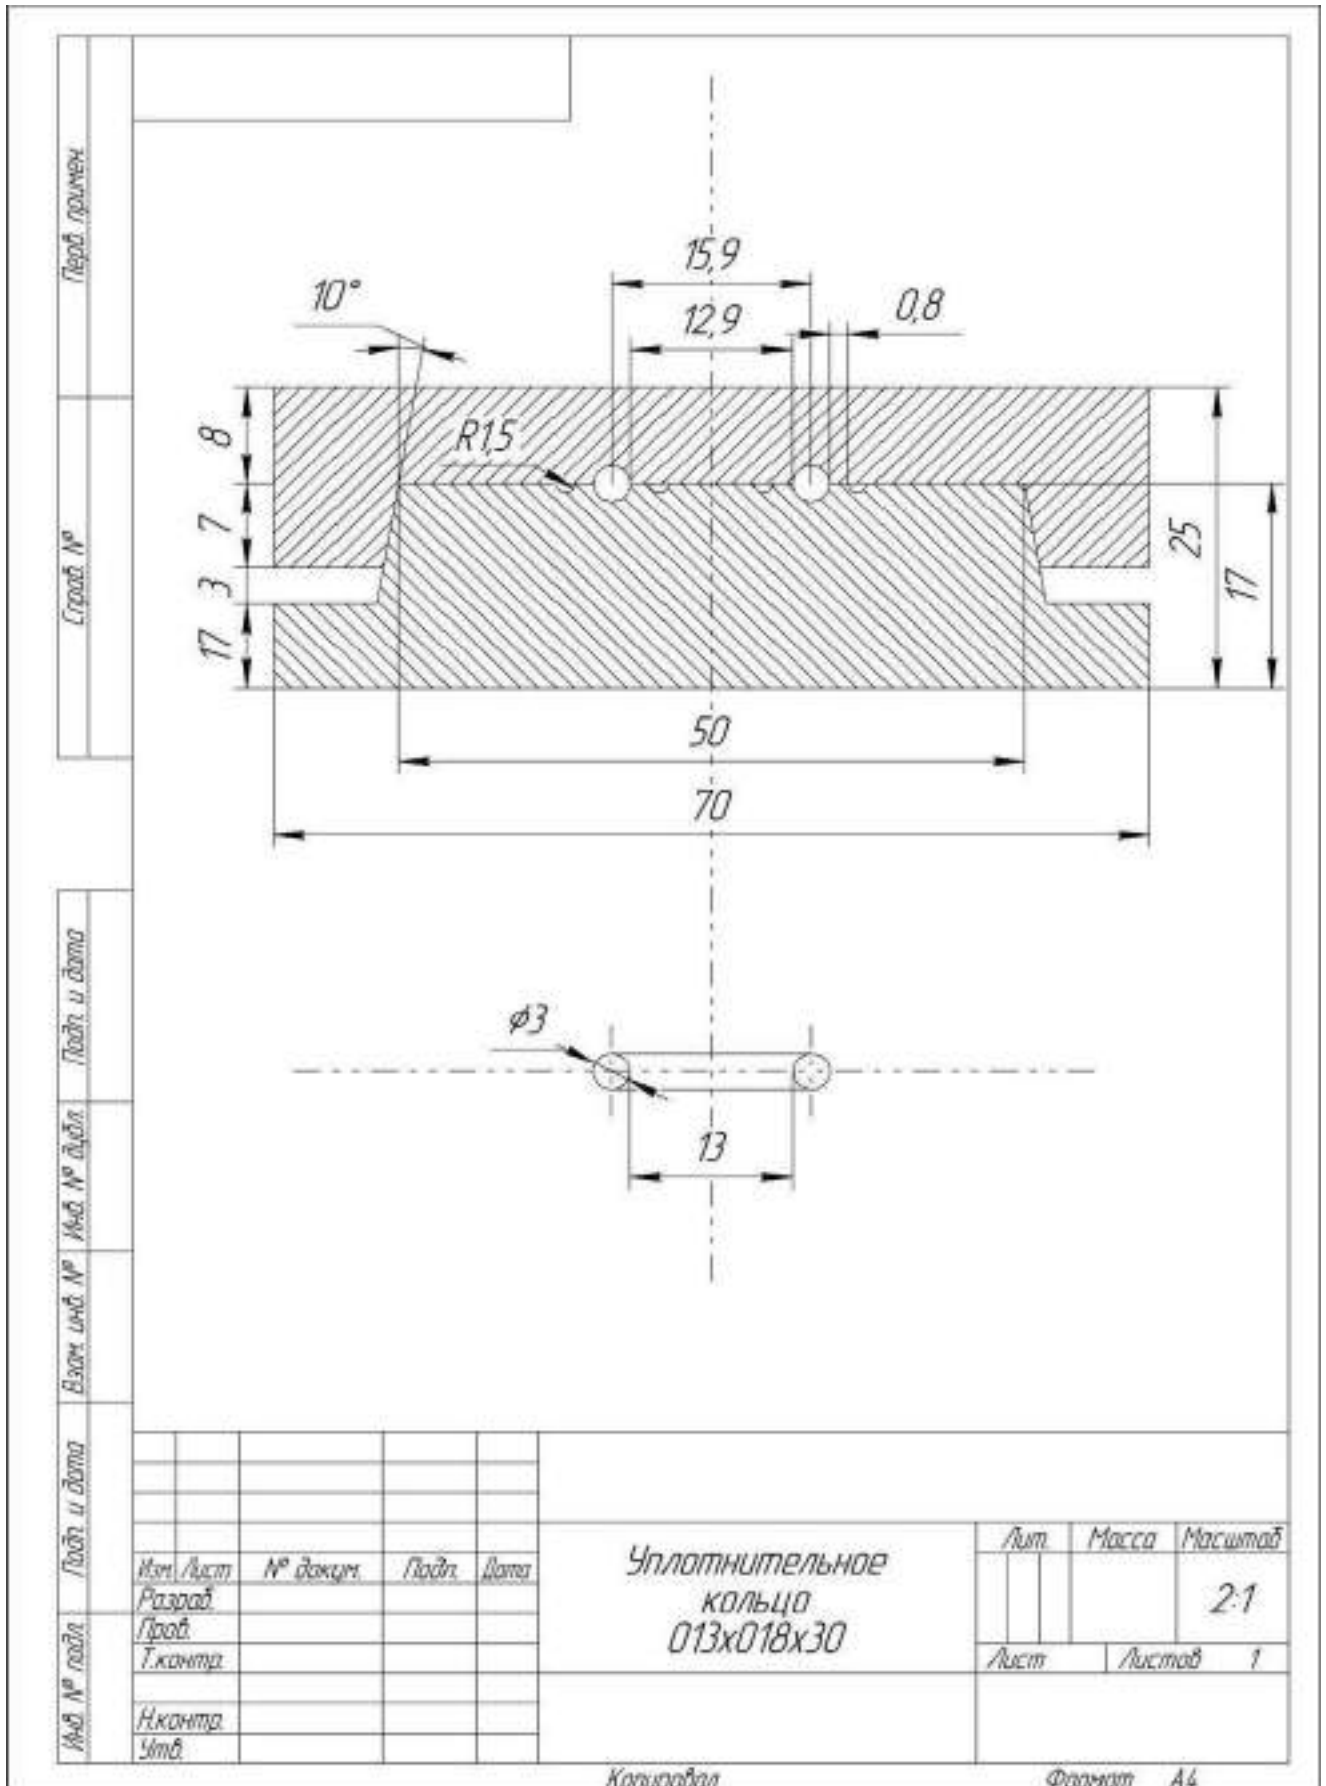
Чертеж пресс-формы для уплотнительного кольца трубки топливной рампы аэродромного тягача Douglas-Kalmar TLB-600
